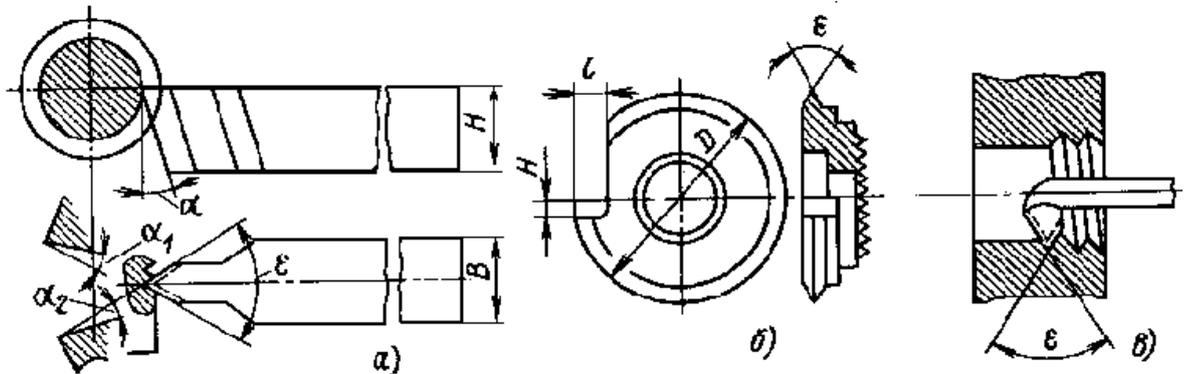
Резьбонарезные резцы: а - прямой, б - круглый, в – изогнутый
